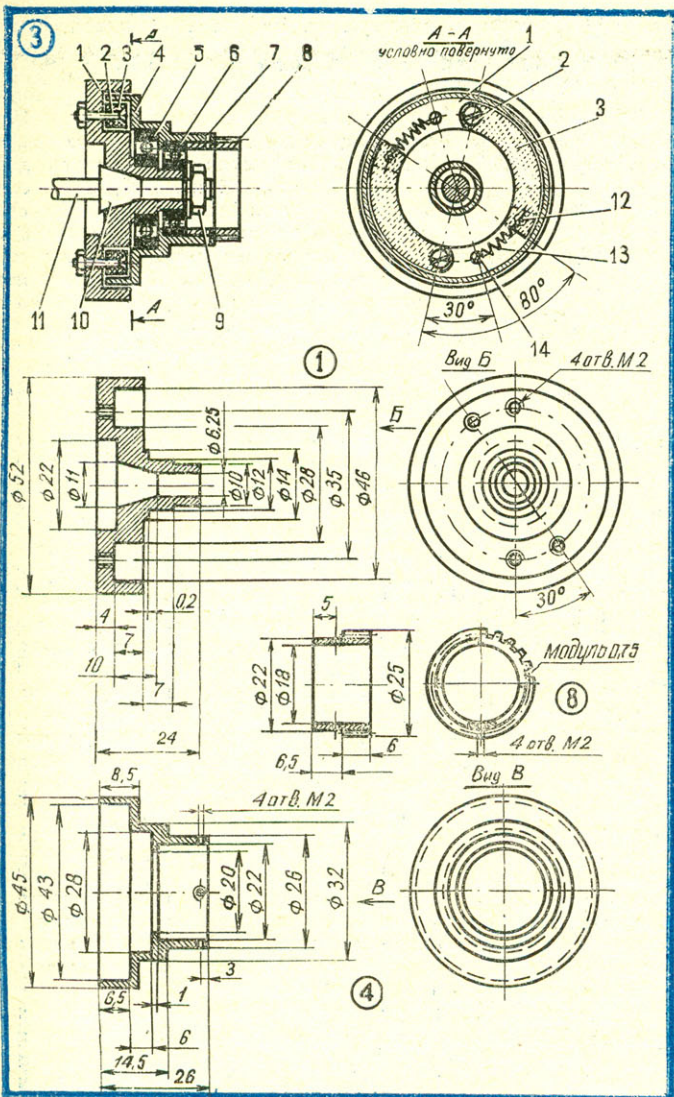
Устройство автоматического сцепления конструкции Е. Петрова (на двигатель типа «Н-В»):
